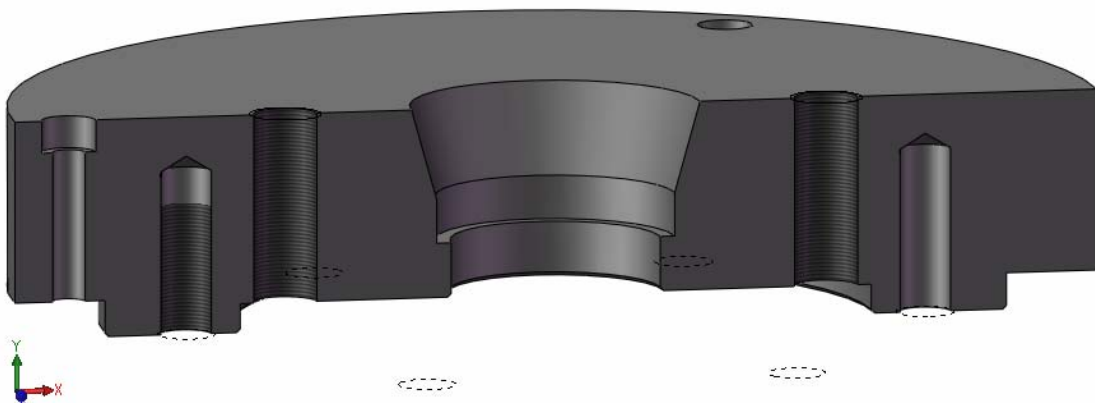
Flansch (ältere Version) mit konischer Bohrung
